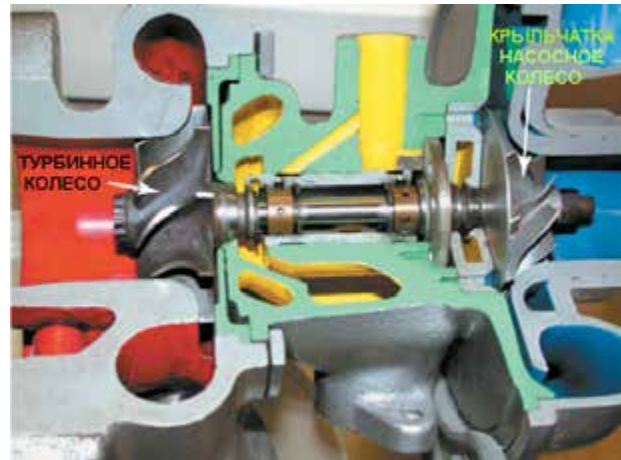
Турбинное колесо, приводимое в движение выхлопными газами (слева), соединено с рабочим колесом нагнетателя (справа) через вал. Втулки, поддерживающие вал, смазываются моторным маслом под давлением; источник: *Pearson Education, Inc.
